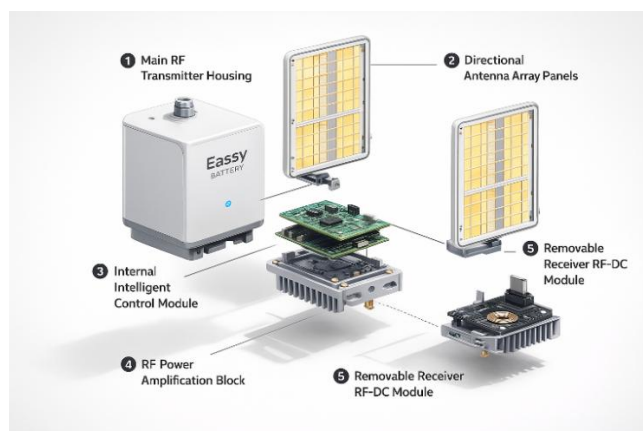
Vista isométrica del cargador inalámbrico con ensamble en explosión.
